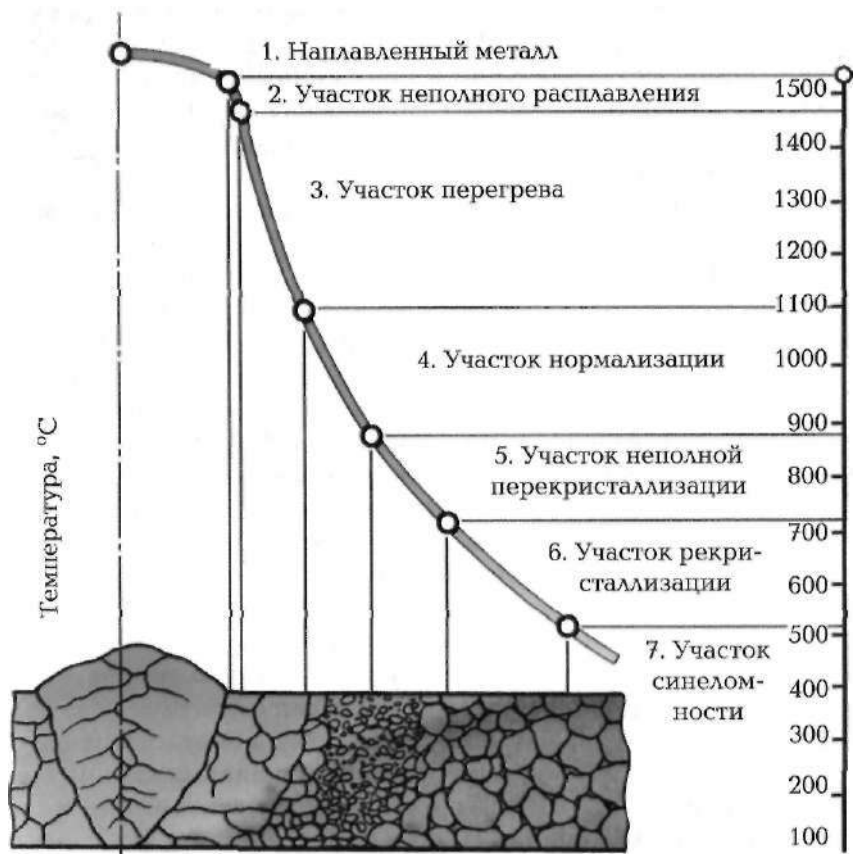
Термический цикл сварного соединения низкоуглеродистой стали при однопроходной сварке
